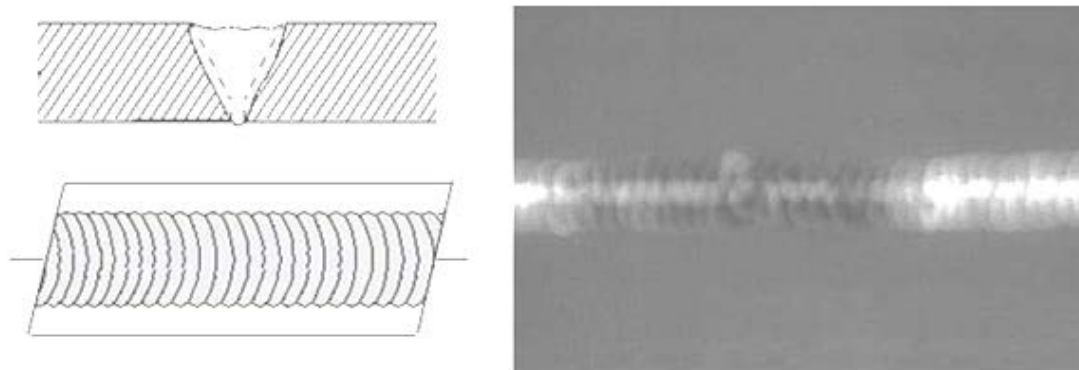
Refuerzo de Soldadura Inadecuado.
